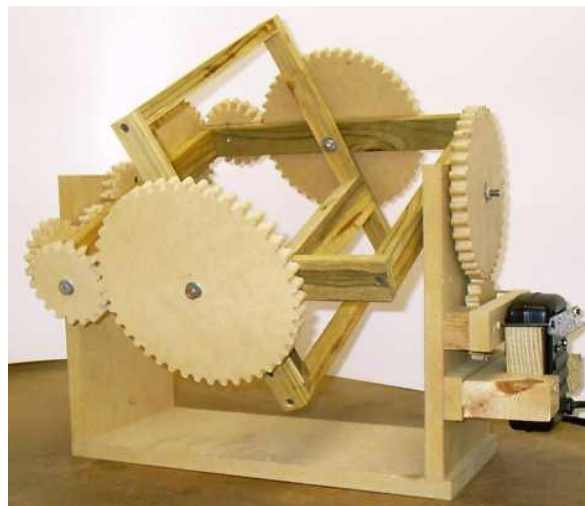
Máquina de moldação por centrifugação em madeira (Steele 2014)
